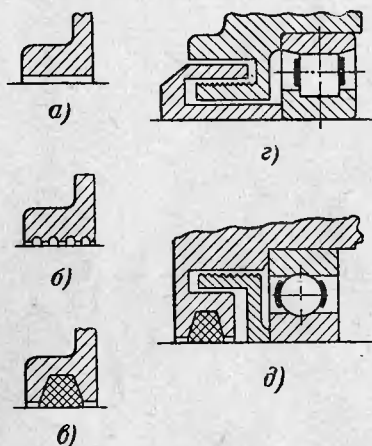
Уплотняющие устройства в подшипниковых щитах.
